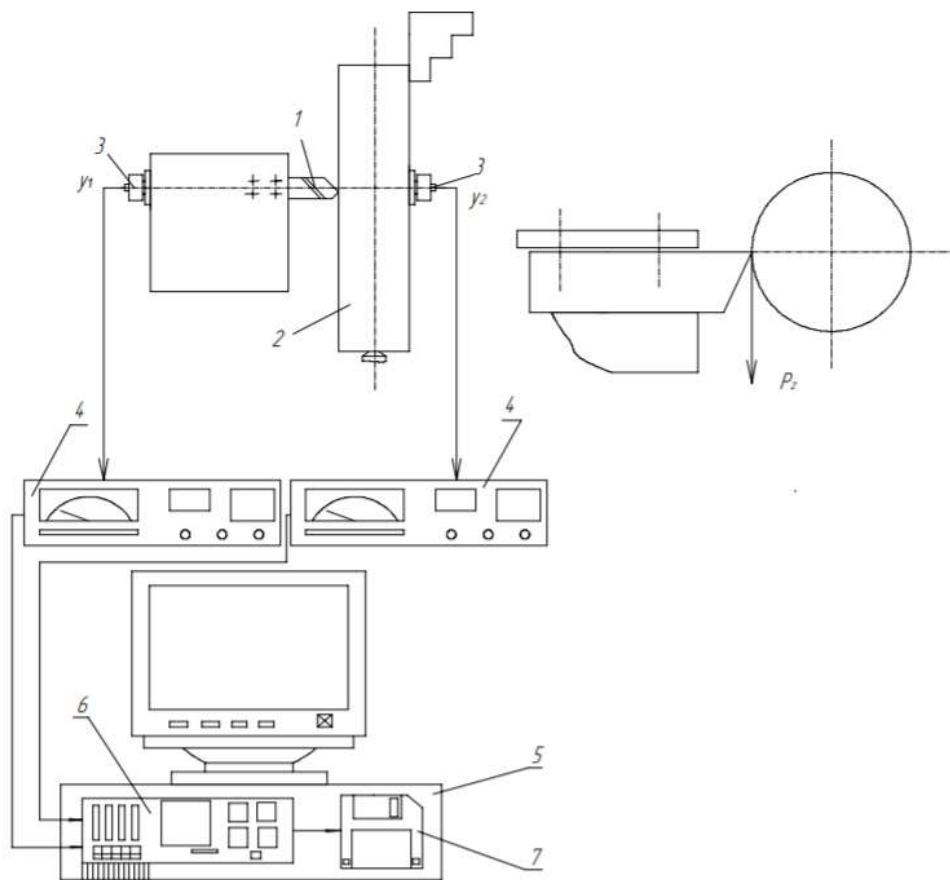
Схема вимірювання коливань у робочій зоні токарного верстата
